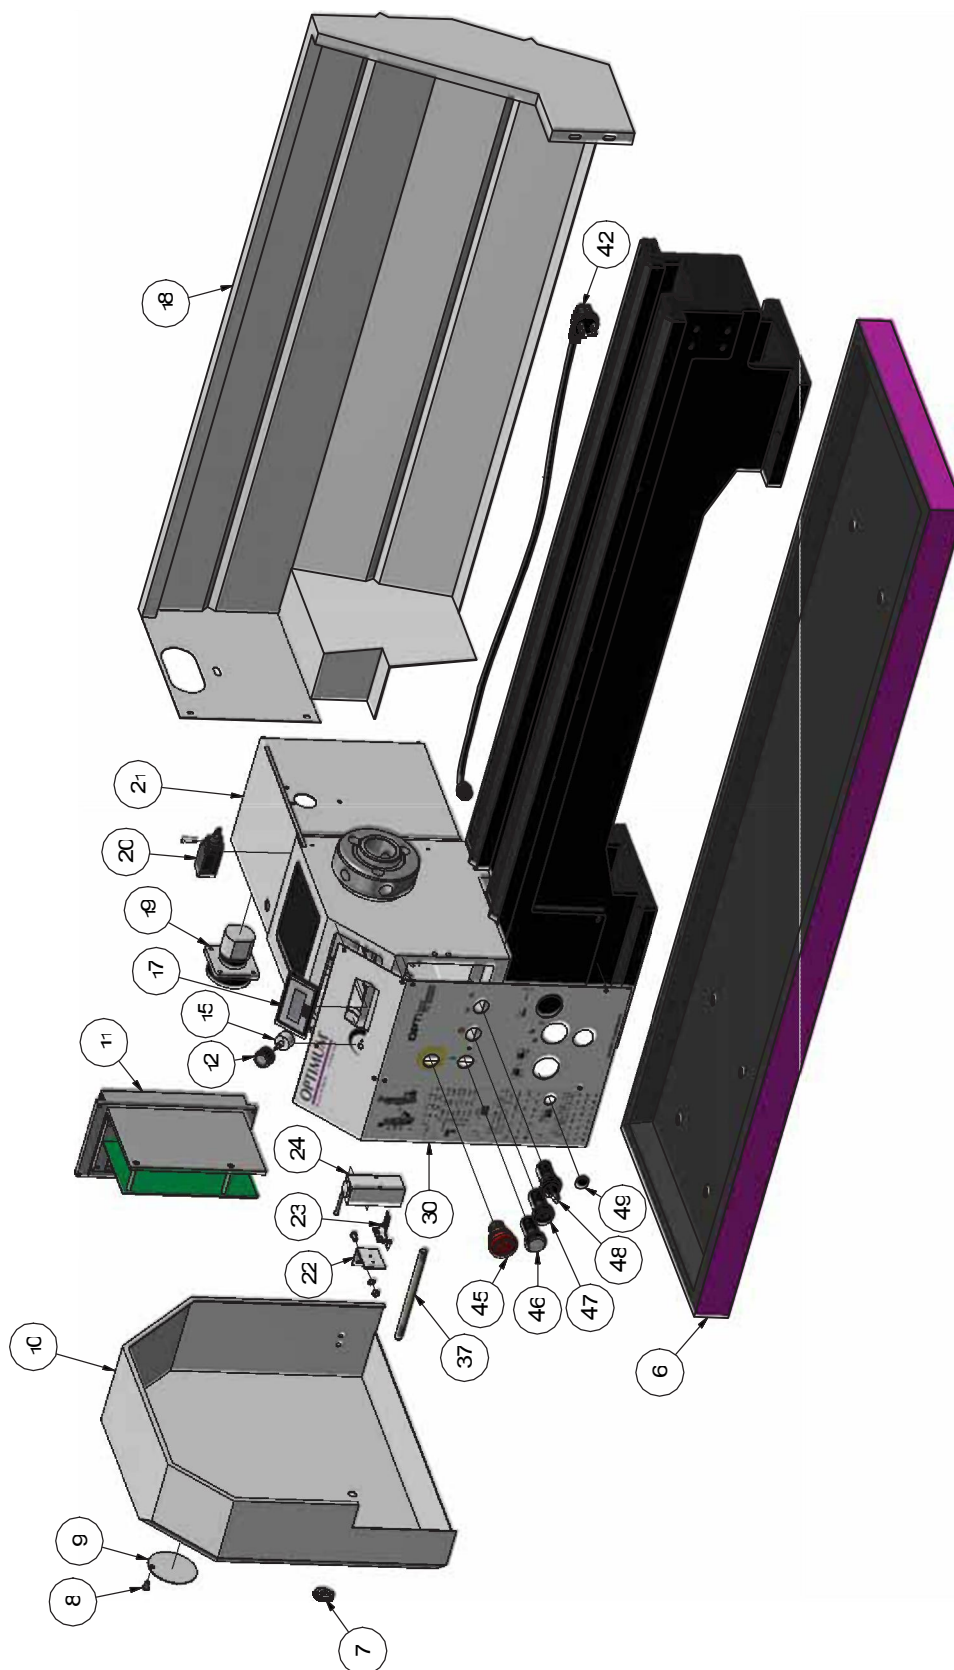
TU3008V - Maschinenbett - Machine bed
